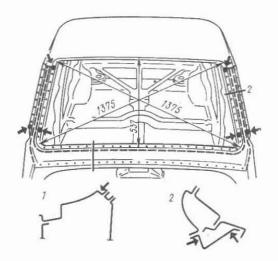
Cambio del panel del marco del parabrisas. Con punteado se indican las líneas de corte, mediante puntos las costuras de soldadura por contacto. En la vista principal se indican con flechas los sitios de soldadura autógena, mediante flechas se indican en los fragmentos los sitios de corte
